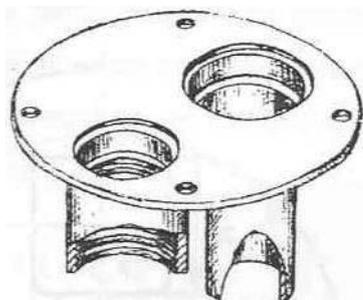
Внешний вид приспособления ШВЕА.301314.025
